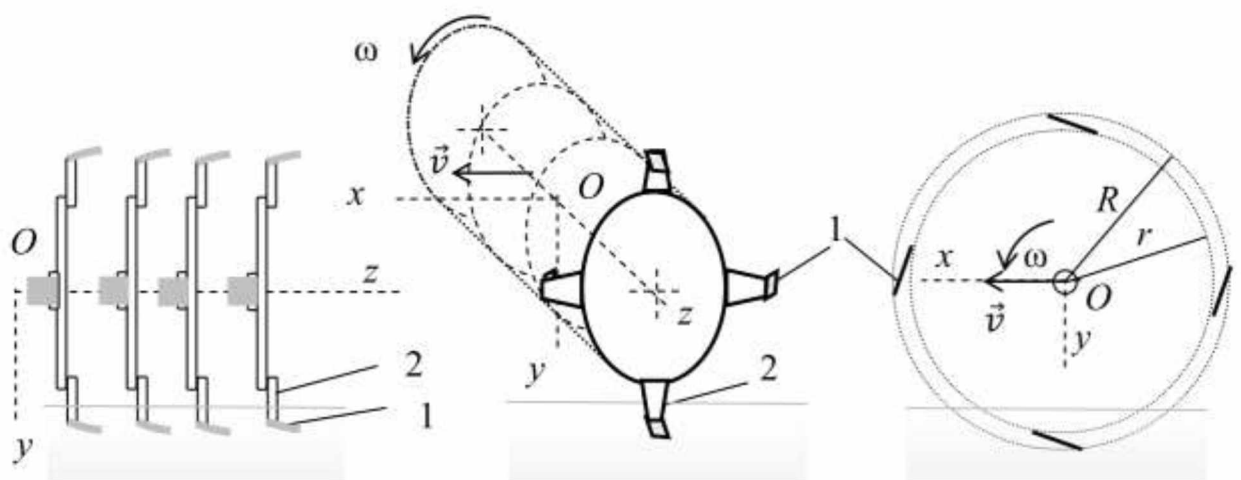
Барабан фрези з ножами 1 і боковинами з ріжучими кромками 2
